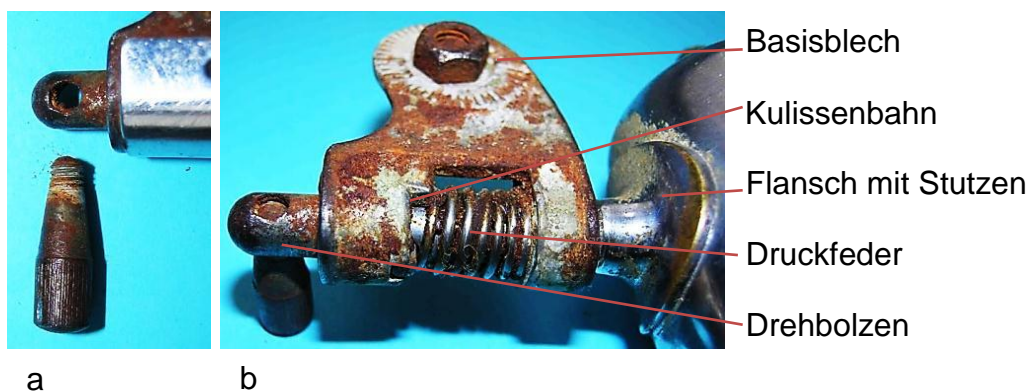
Kippvorrichtung: a) Einschraubbarer Bedienungshebel, b) Drehbolzen mit Flansch
